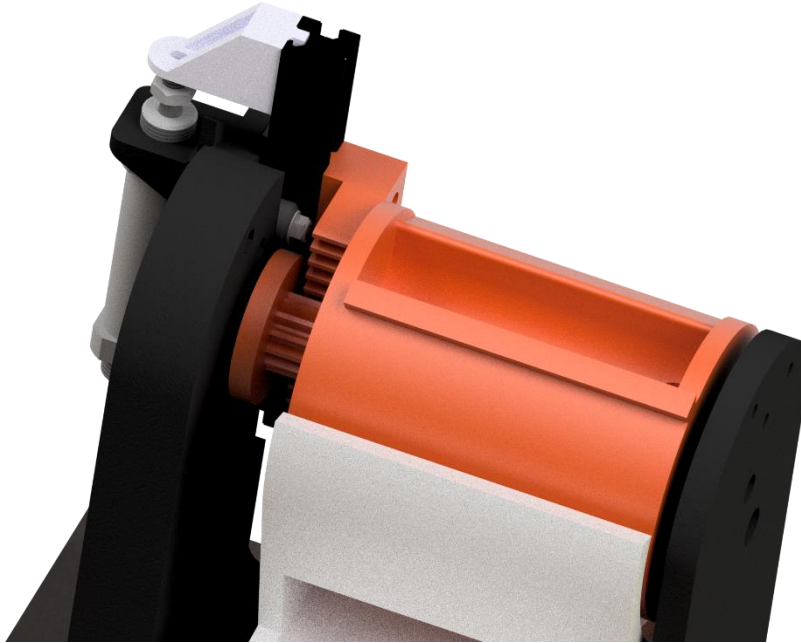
Vista detallada del mecanismo piñón-cremallera del alimentador de piezas.
